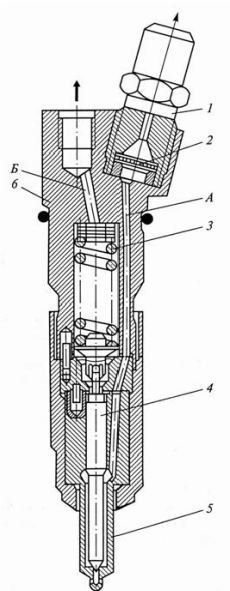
Закрита форсунка з пружинними запиранням: 1 – штуцер; 2 – захисний фільтр; 3 – пружина; 4 – голка розпилювача; 5 – корпус розпилювача; 6 – корпус форсунки; А – підвідний канал; Б – відвідний канал
